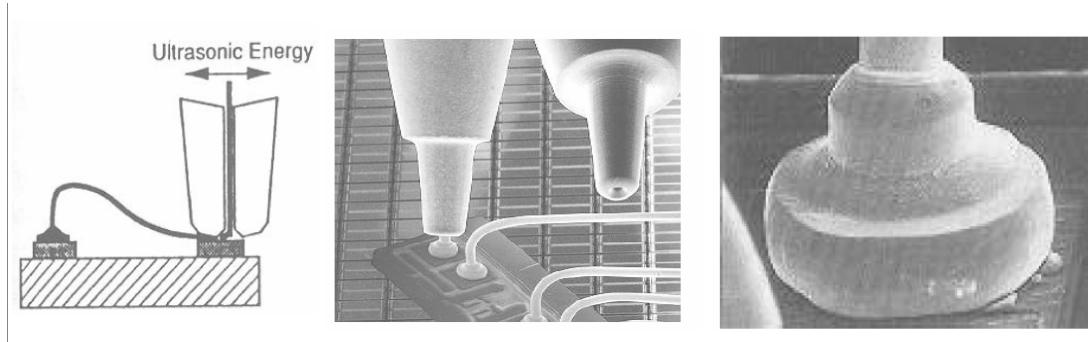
Report de contact par la technique du " ball bonding " (soudure thermo-sonique)
